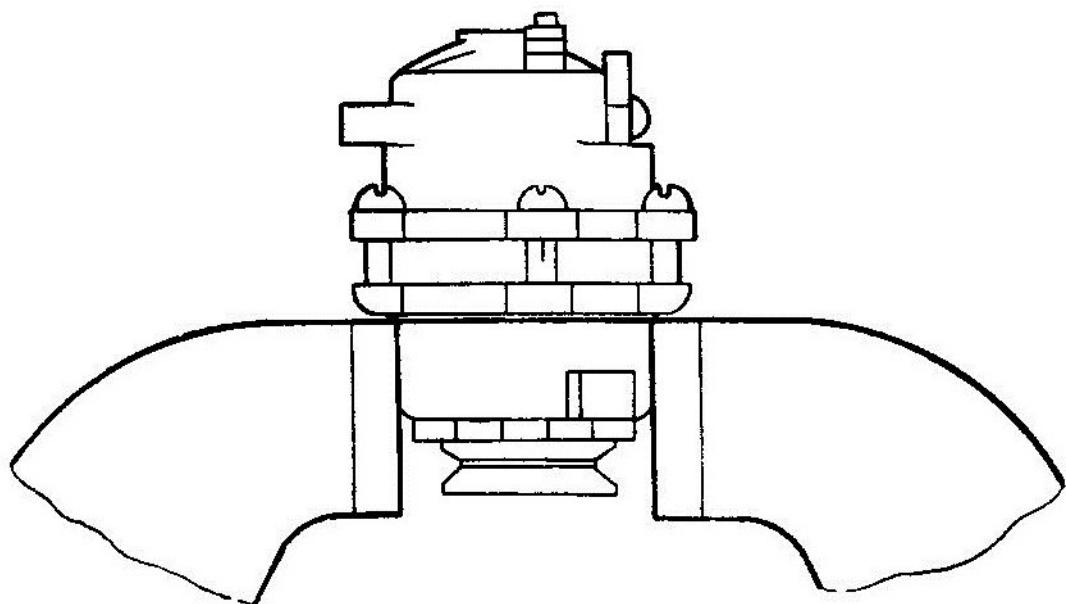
Закрепление генератора Г250-А1 во время разборки
